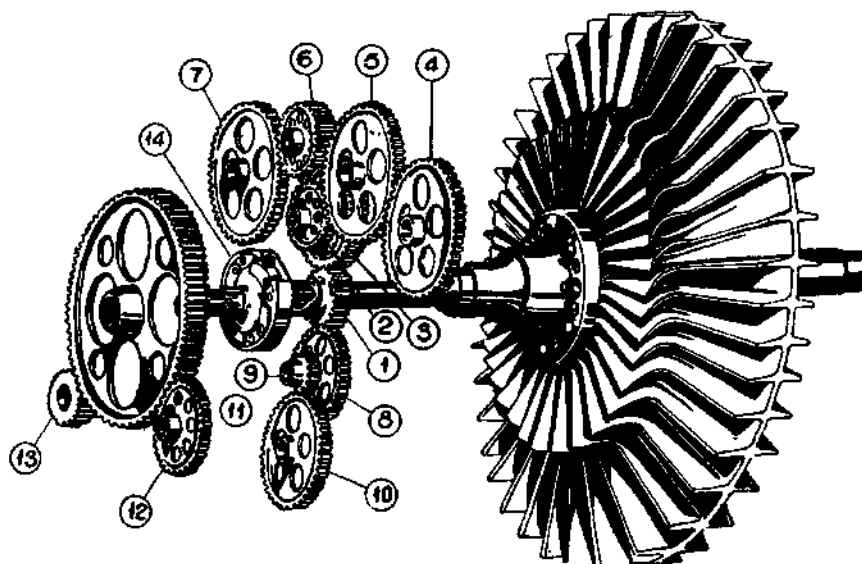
I. Sistema de engranajes en el General Electric I-40. 1, piñón principal; 2, piñón superior; 3, piñón intermediario; 4, piñón de mando del regulador de alimentación; 5, piñón de la bomba de combustible; 6, piñón del generador; 7, piñón del tacómetro; 8, piñón intermediario inferior; 9, piñón inferior; 10, piñón de mando de la bomba de lubricación; 11, corona para los mecanismos de puesta en marcha; 12, piñón de mando de la bomba de combustible de puesta en marcha; 13, piñón del eje del motor de arranque; 14, embrague de la puesta en marcha.
